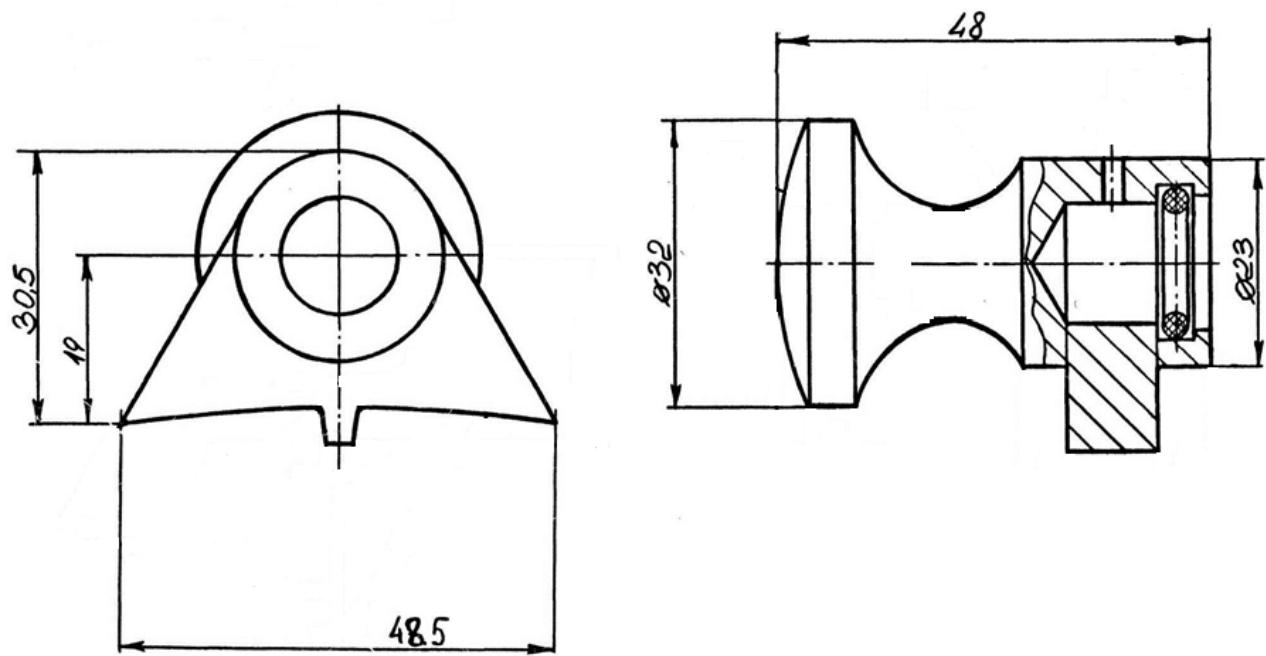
ЗМ 7820-4550, Фиксатор коленчатого вала
